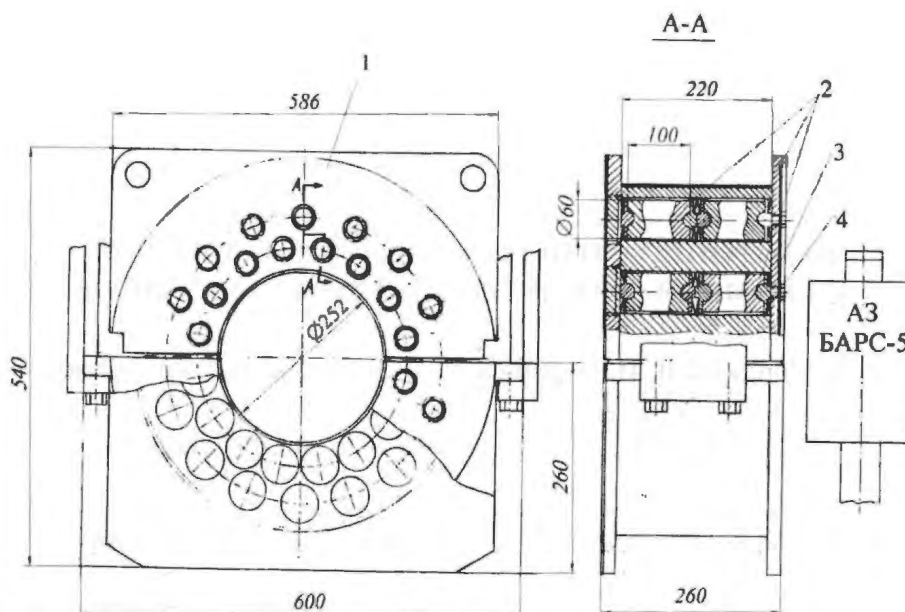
Схематическая конструкция реактора-бустера: 1 – верхний блок; 2 – стержни из делящегося материала; 3 – толкатель; 4 – пружина
